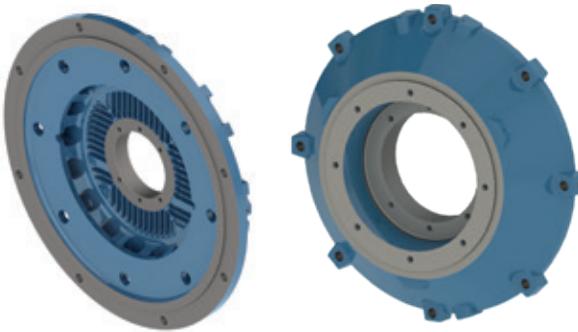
Tampa dianteira - Flange "FF" e Flange "C".
